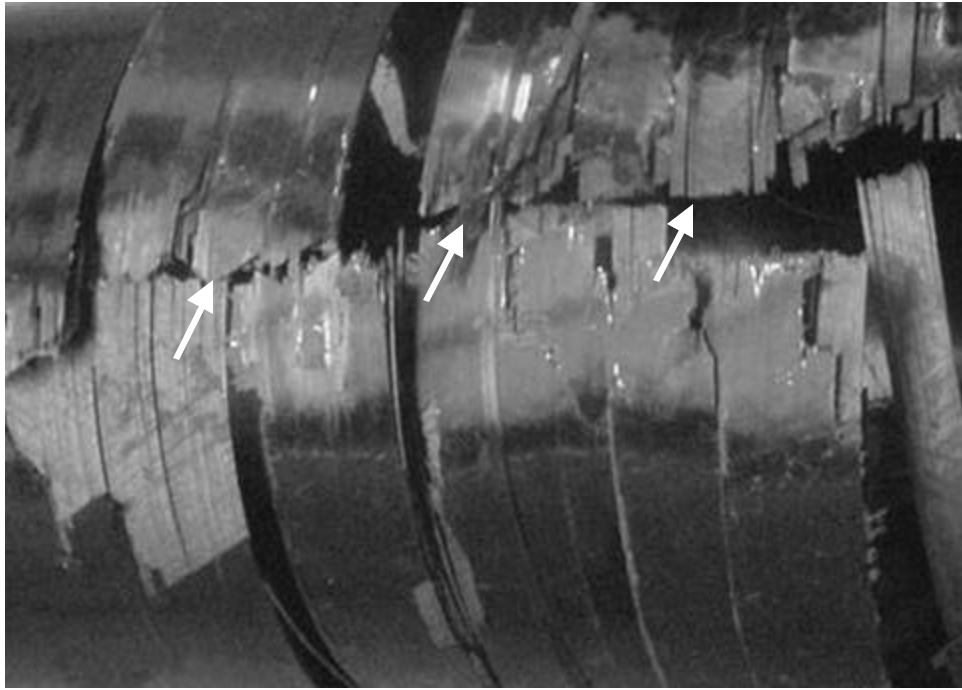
Aspecto final de um cilindro com bobinagem simétrica após ensaio hidrostático.
